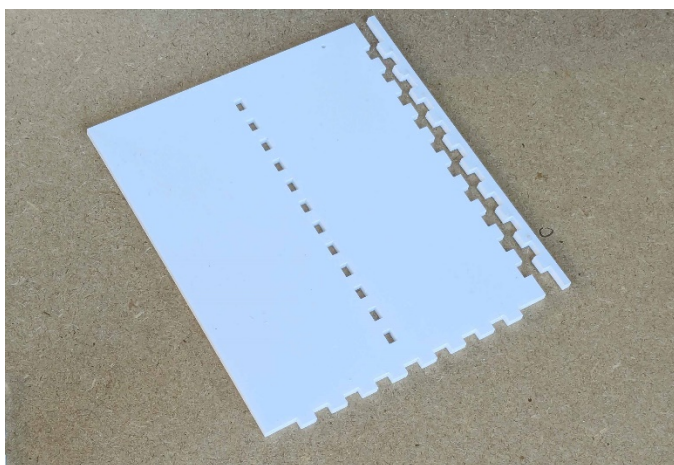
Montage des supports de glissières de la trappe arrière sur un côté
